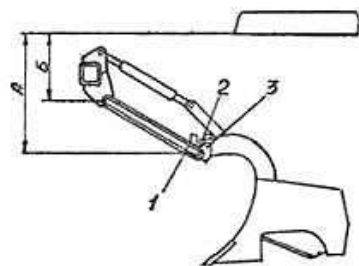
Схема установки обмеження опускання: 1 – стопор; 2 – контрґайка тяги підвіски; 3 - болт
